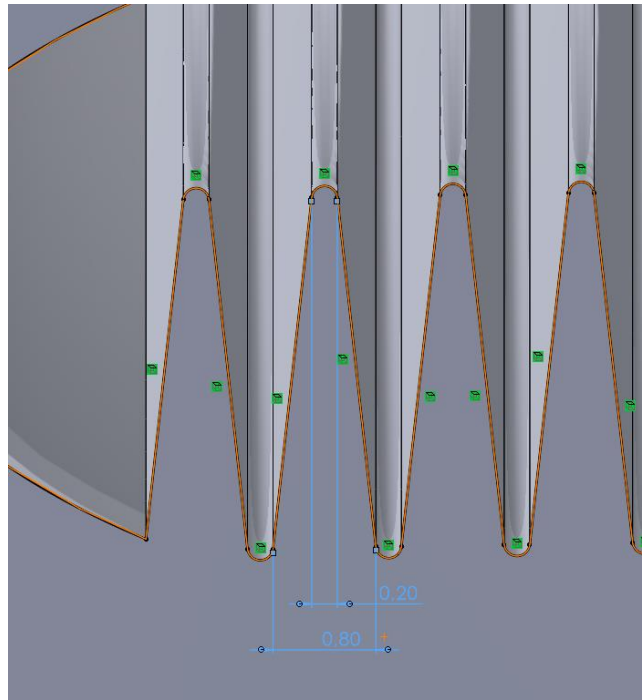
Pormenor da geometria das alhetas trapezoidais
